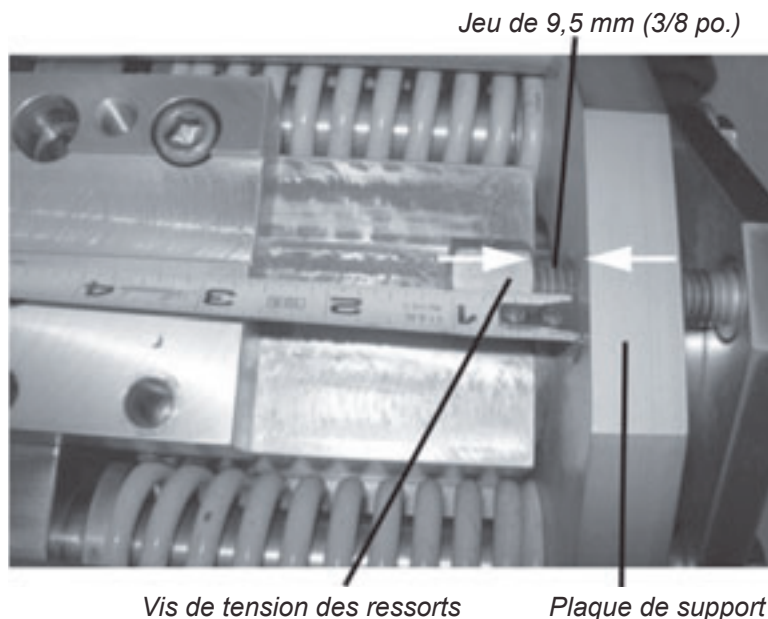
Réglez à nouveau la vis de tension du ressort en laissant un jeu de 3/8 po. (9,5 mm) avec la plaque de support.
